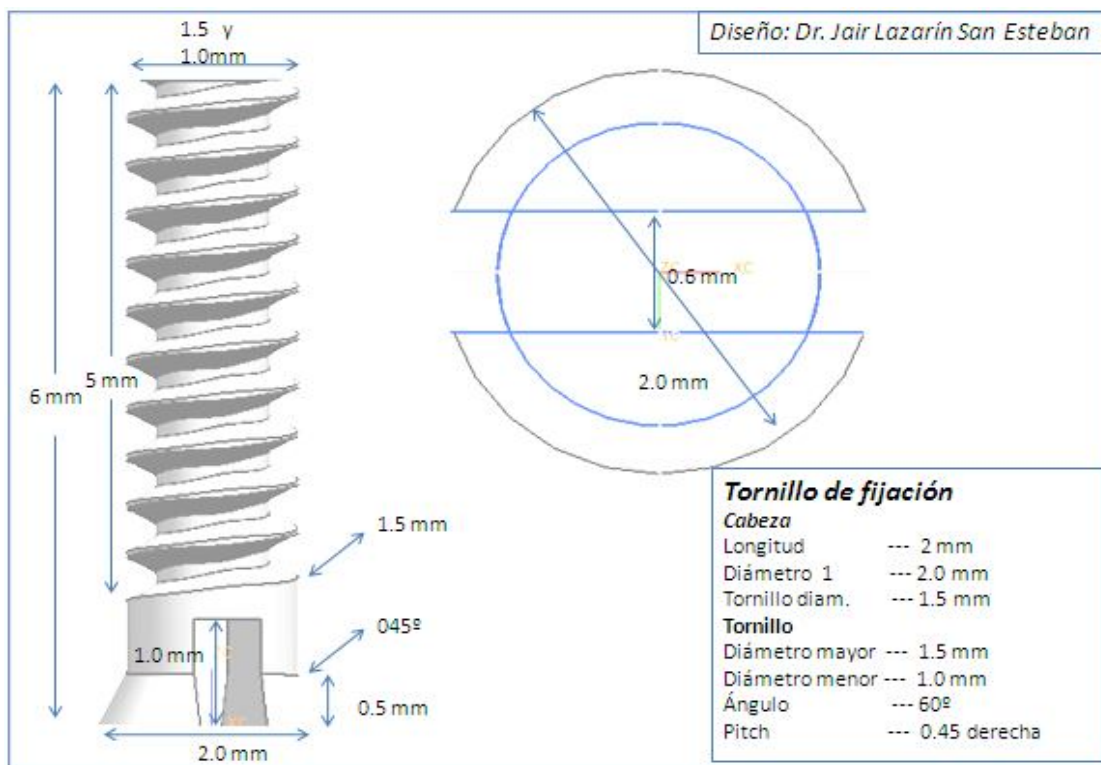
Dimensiones del conector menor con cuerda para ensamblarse a los anclajes
